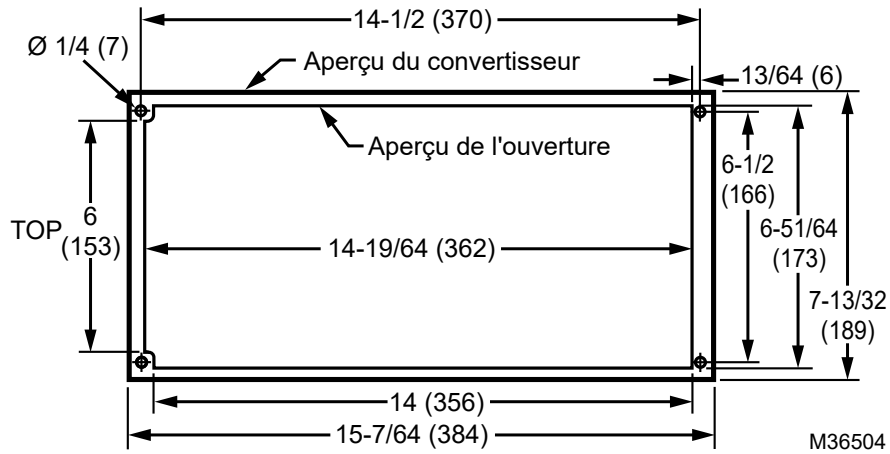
Schéma des dimensions en montage par bride, pour MI4 [unité : pouces (mm)]
